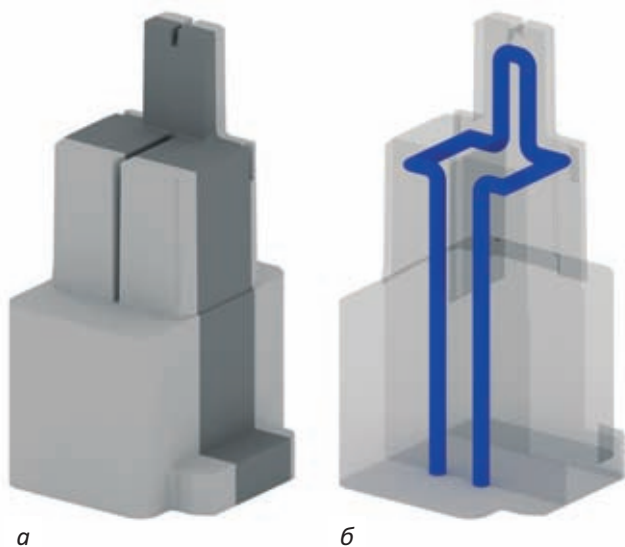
Внешний вид (а) и внутренняя структура (б) формообразующей вставки для формы, изготовленной по технологии диффузионной сварки
